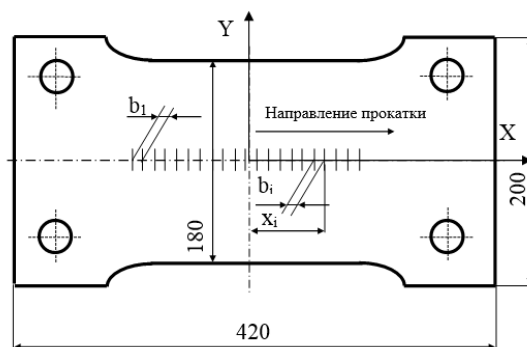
Заготовка для испытания на трение по методу обтяжки
